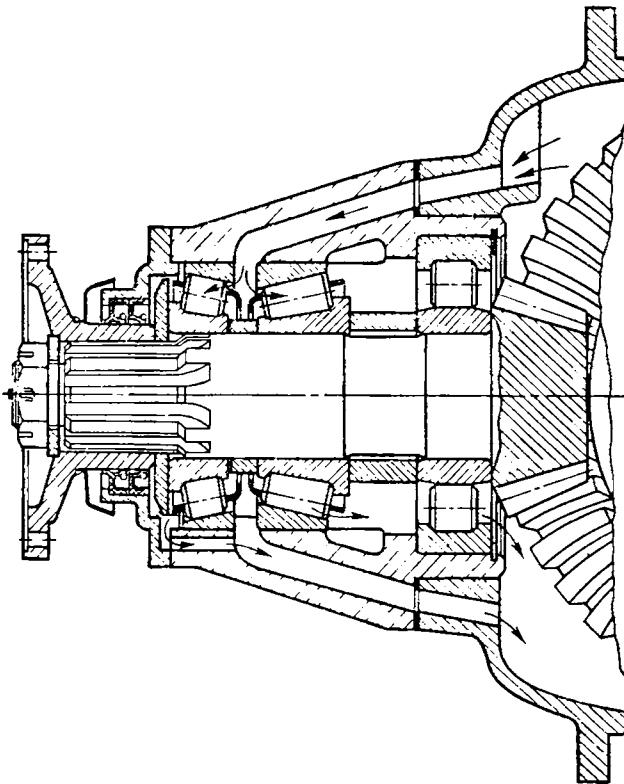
Схема смазки подшипников ведущей шестерни главной передачи
